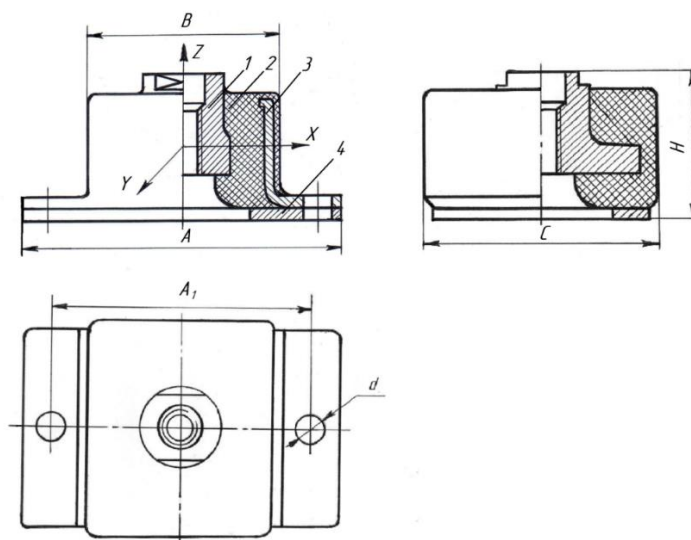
Конструкция виброизолятора типа АКСС – М: 1 – несущая планка; 2 – резиновый массив; 3 – скоба; 4 – опорная планка; А – габаритная ширина виброизолятора; В – ширина виброизоляционного массива; С – толщина виброизолятора; Н – высота виброизолятора; А<sub>1</sub> – расстояние между центрами крепежных отверстий; d – диаметр крепежного отверстия
